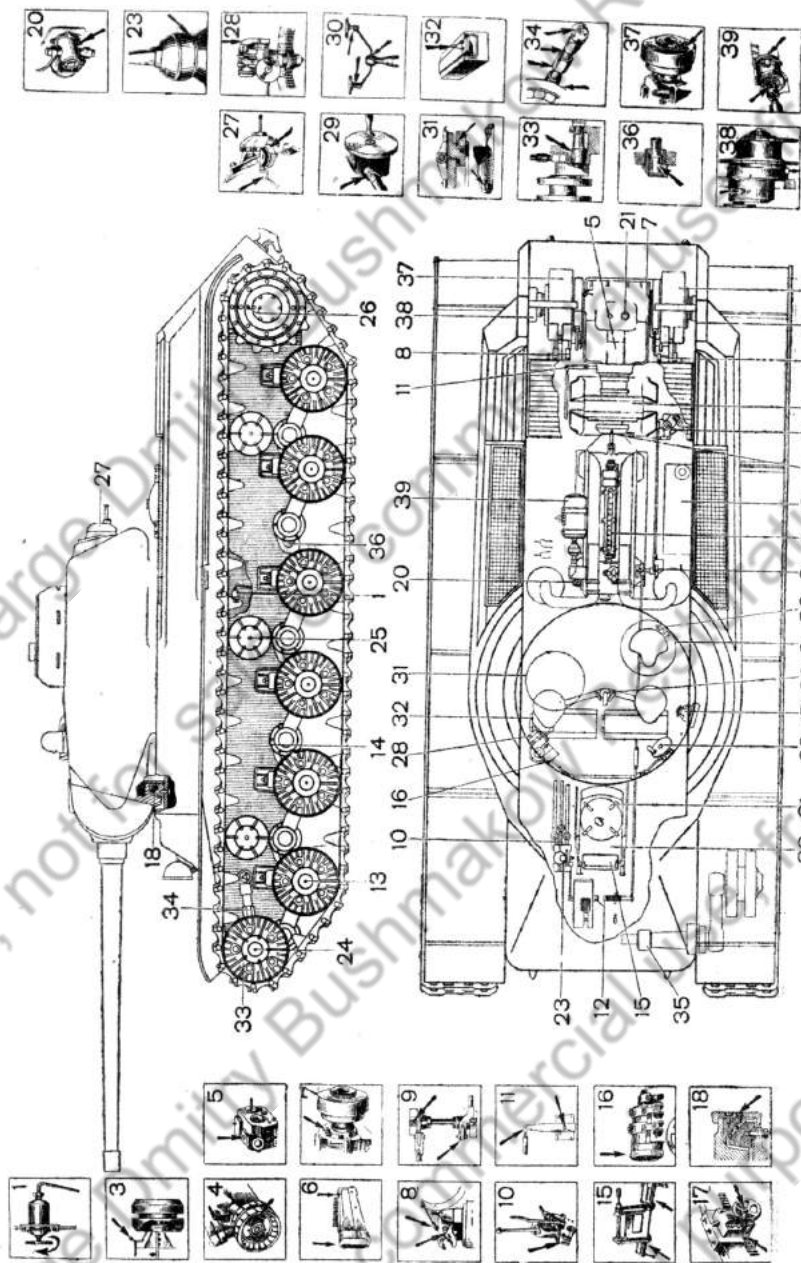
Схема точек смазки агрегатов и механизмов танка
